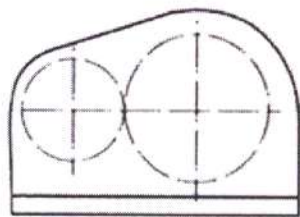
Схема цилиндрического одноступенчатого горизонтального редуктора.
